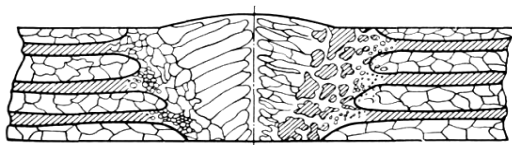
Схема структуры металла сварного соединения
